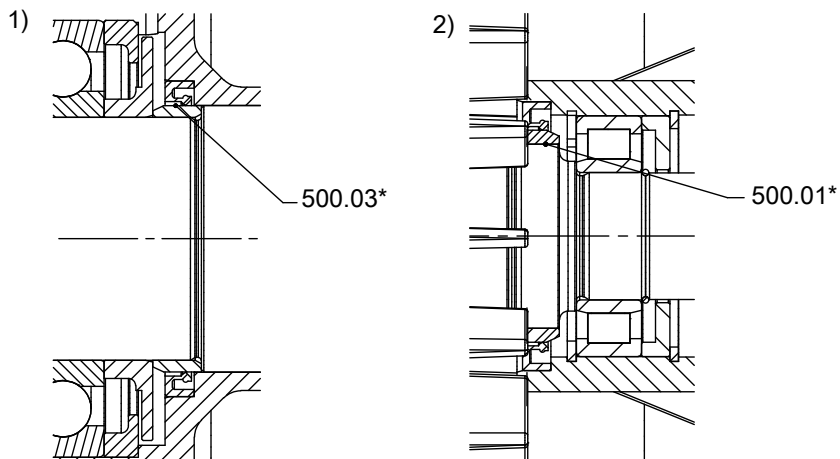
Подшипниковые опоры — насосный агрегат с системой охлаждения
